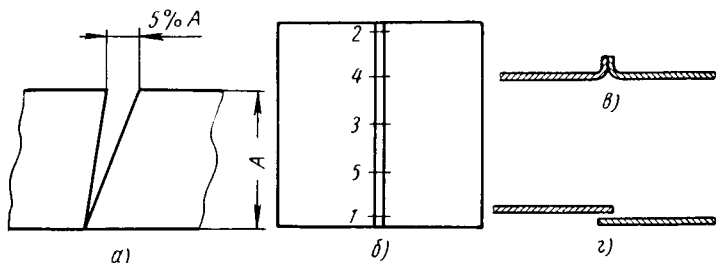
Соединение сваркой тонкой листовой стали
